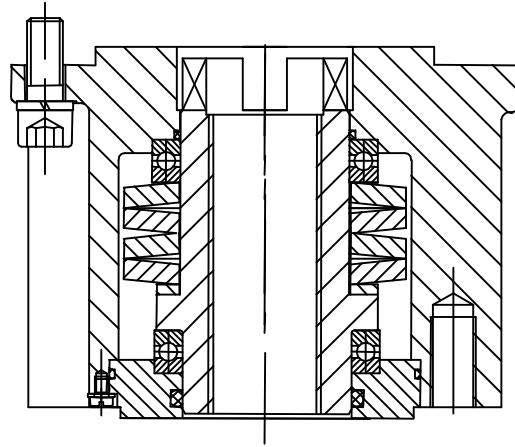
高速缓冲推力盘 Fig. 4 High speed buffering thrust attachment
